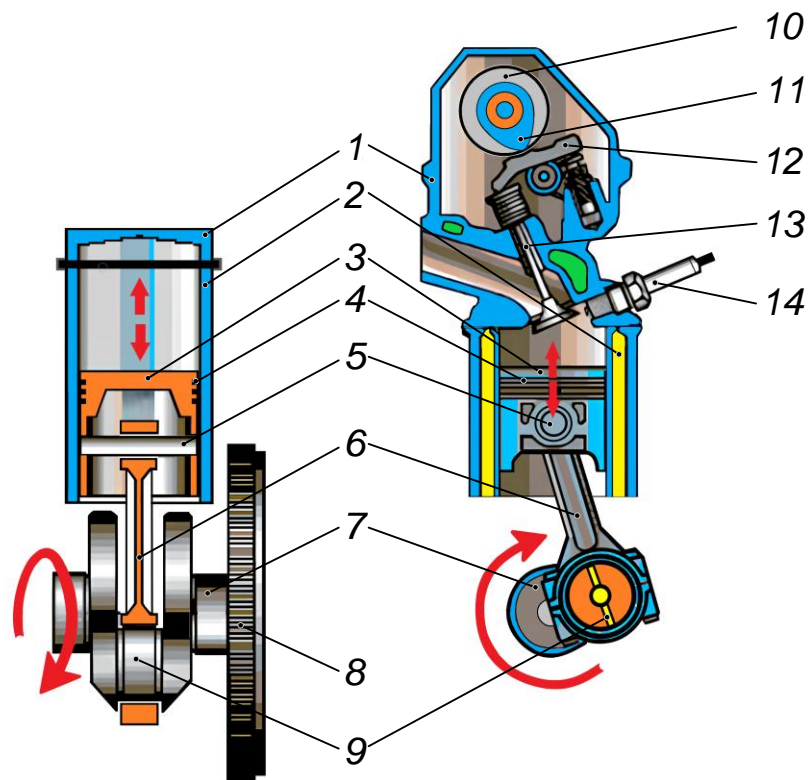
Будова ДВЗ карбюраторного типу: 1 – головка циліндра; 2 – циліндр; 3 – поршень; 4 – поршневі кільця; 5 – поршковий палець; 6 – шатун; 7 – колінчастий вал; 8 – маховик; 9 – кривошип; 10 – розподільний вал; 11 – кулачок розподільного валу; 12 – важіль; 13 – клапан; 14 – свічка запалювання
